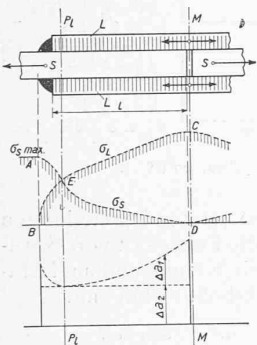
Stab mit Fuge; Flacheisen in Stirn- und Flankennähten angeschweisst.
